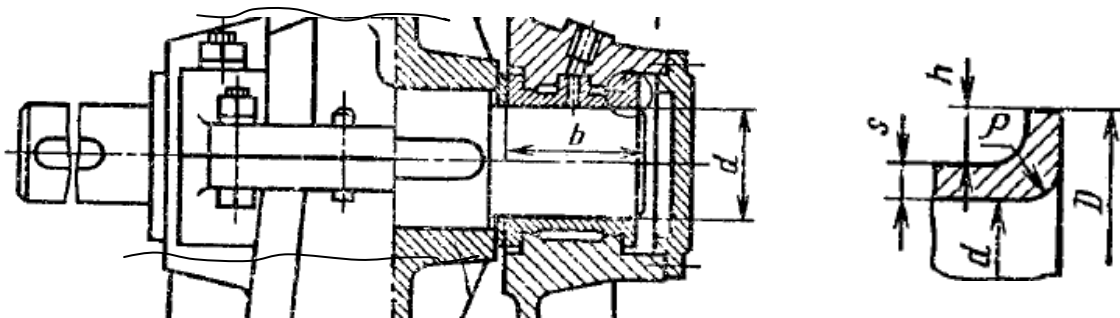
Тихоходный вал червячного редуктора на опорах с подшипниками скольжения
